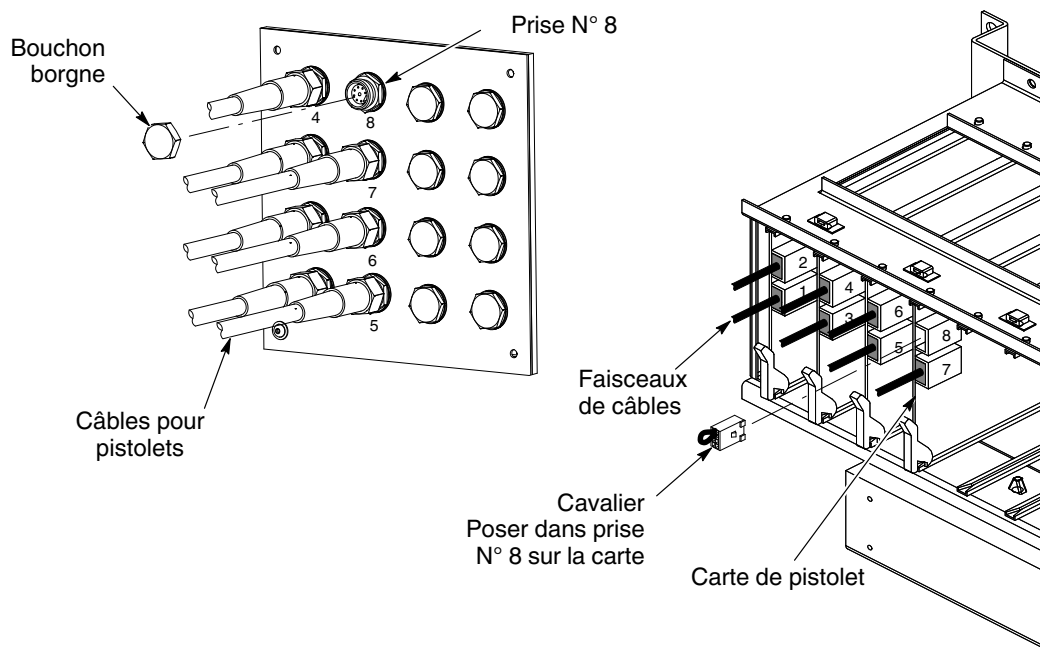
Pose du bouchon et du cavalier – Exemple illustrant un système à 8 pistolets avec 7 pistolets
